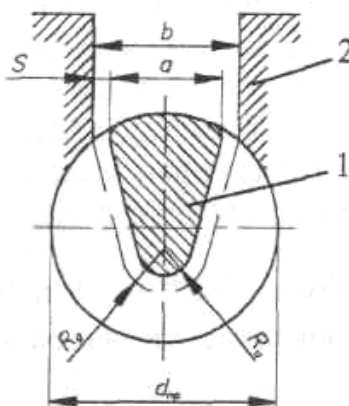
Схема, поясняющая влияние износа проволочного электрода-инструмента на точность обрабатываемого паза в заготовке
